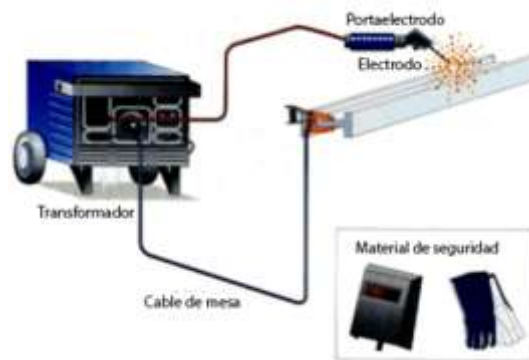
Esquema de soldadura por arco eléctrico.
